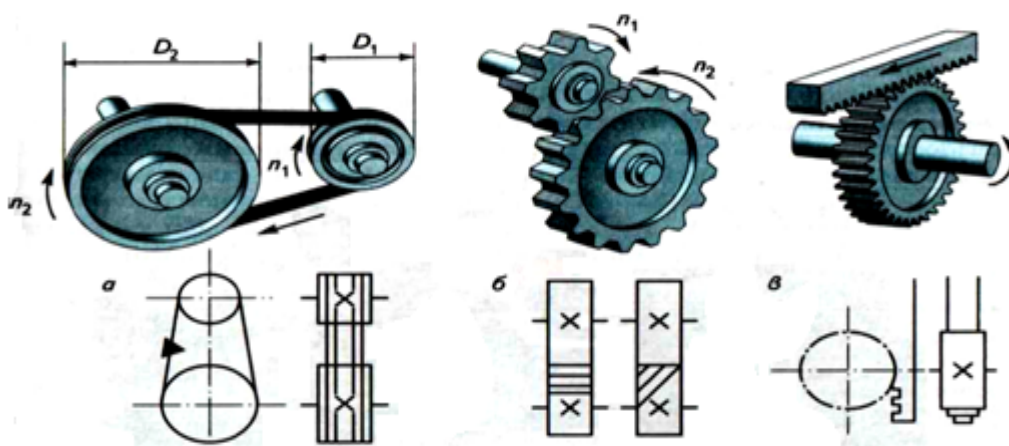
Виды механических передач, применяемых в токарном станке, и их условные обозначения: а – ременная; б – зубчатая; в – реечная
